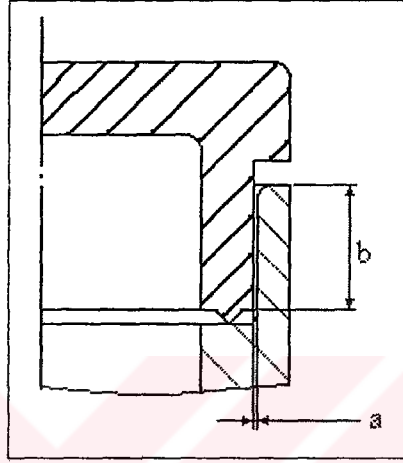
Girintili ve Çıkıntılı parçalarda gerilme yoğunlaşmasının olduğu bölgeler
